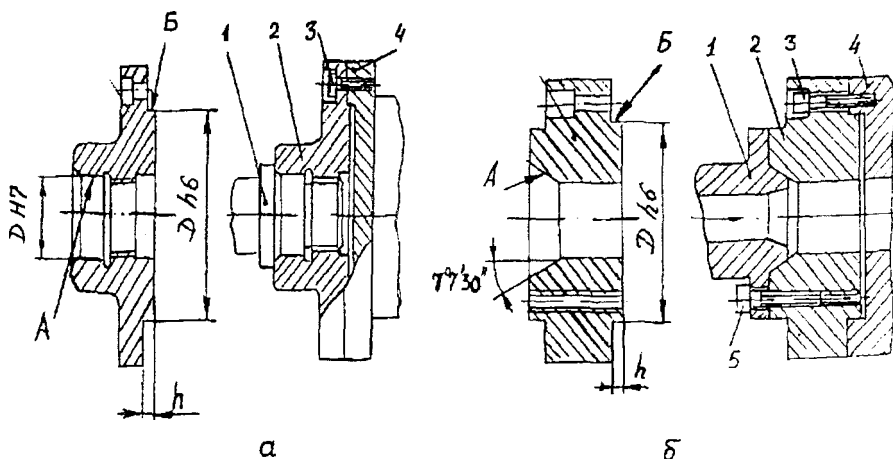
Установка приспособления на переходный фланец с центрирующим цилиндрическим пояском (а) и с коническим пояском (б) на токарном станке: 1 — шпиндель; 2 — переходный фланец; 3 — винт; 4 — корпус приспособления; 5 — винт
